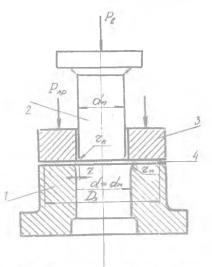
Рис. I. Конструктивная схема жесткого штампующего инструмента (штампа) для первой операции вытяжки
